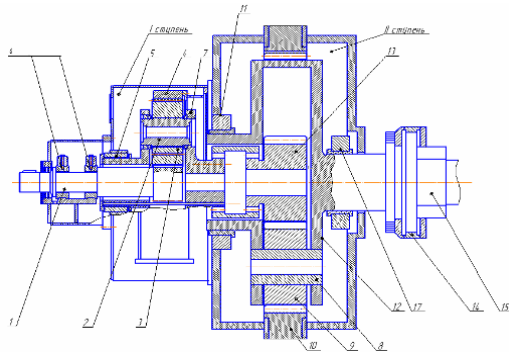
Планетарный редуктор предлагаемой конструкции (1 вариант): 1 - вал-шестерня I ступени; 2,8 - ось сателлита; 3,9 - сателлит; 4,10 - зубчатый венец; 5,11,16,17 - подшипники скольжения водила; 6 - подшипники скольжения вала-шестерни I ступени; 7,12 - водило; 13 - солнечная шестерня II ступени; 14 - зубчатая муфта; 15 - промвал
